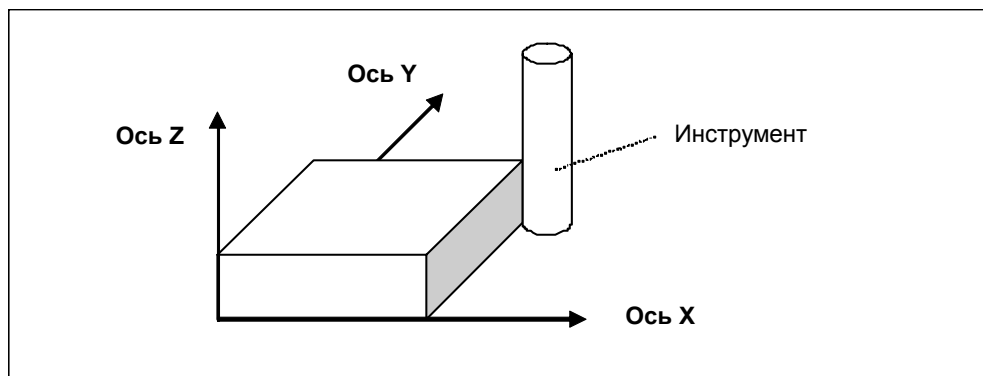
(o) Коррекция на режущий инструмент, когда отсутствует погрешность установки заготовки
